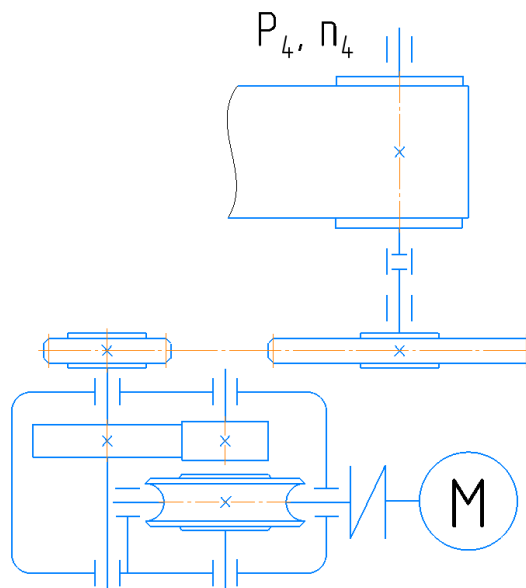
Кінематична схема триступінчатого черв'ячного редуктора з приводним барабаном
